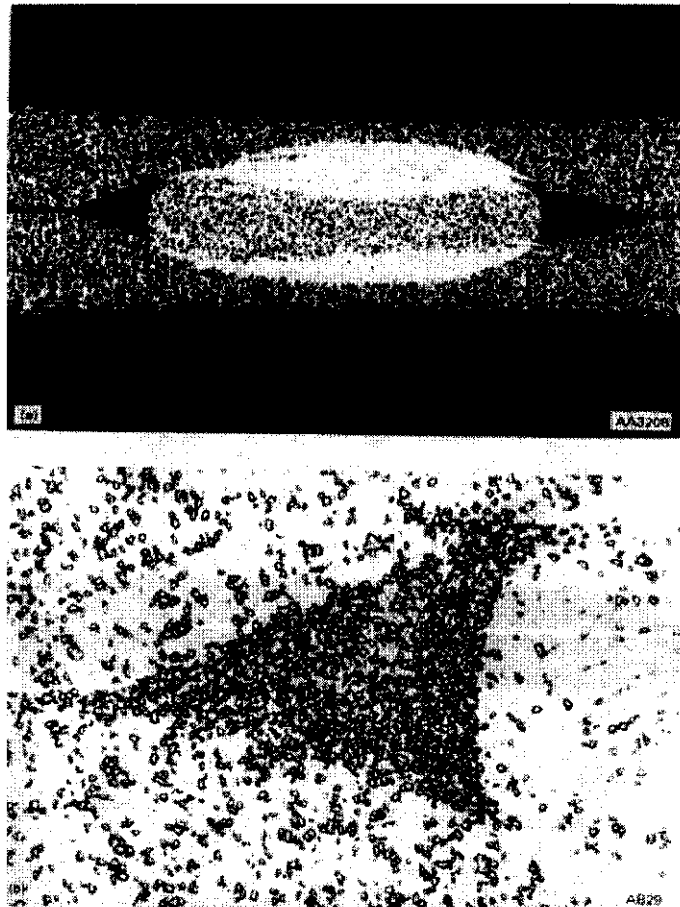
Soldadura por resistencia de 6082/SiC/20p. a) Botón, b) Detalle (114)
